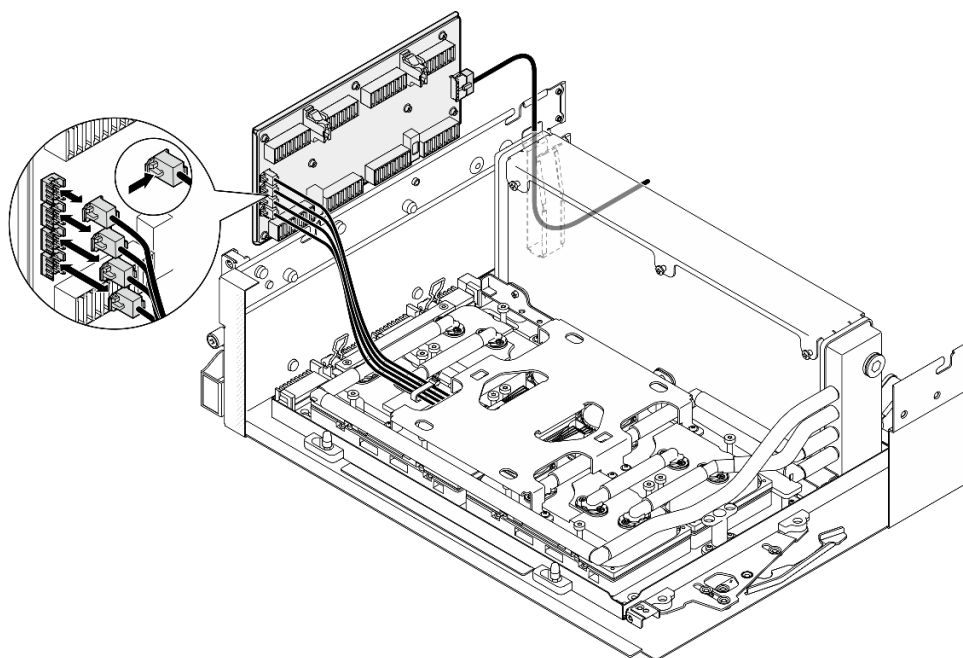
Conexión del cable de la bomba del conjunto de la placa de frío
